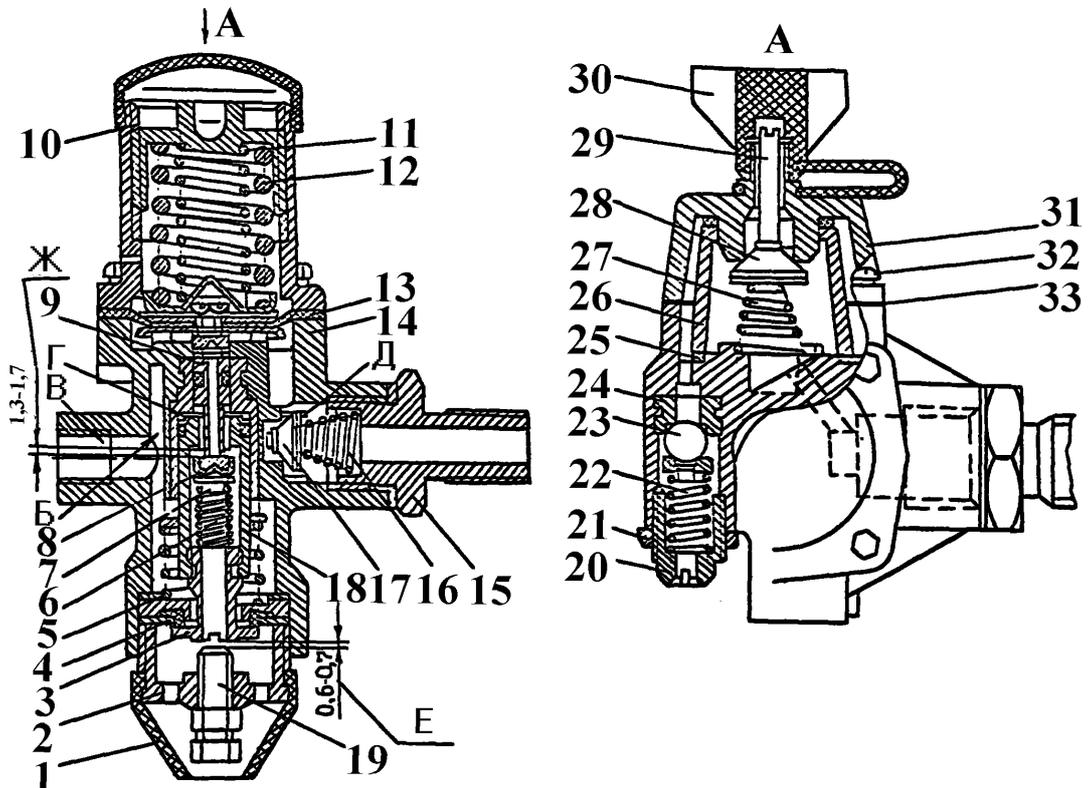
Регулятор давления: 1 - насадка; 2 - крышка; 3 - разгрузочный клапан; 4 - втулка; 5, 6, 11, 12, 16, 22, 27 - пружины; 7 - направляющая клапана; 8 - атмосферный клапан; 9 - поршень; 10, 31 - крышки; 13 - диафрагма; 14 - корпус; 15 - штуцер; 17 - обратный клапан; 18 - поршень; 19 - болт; 20, 32 - винты; 21 - гайка; 23 - шарик; 24 - седло; 25 - прокладка; 26 - фильтр; 28 - клапан отбора воздуха; 29 - стержень; 30 - гайка-барашек; 33 - прокладка
